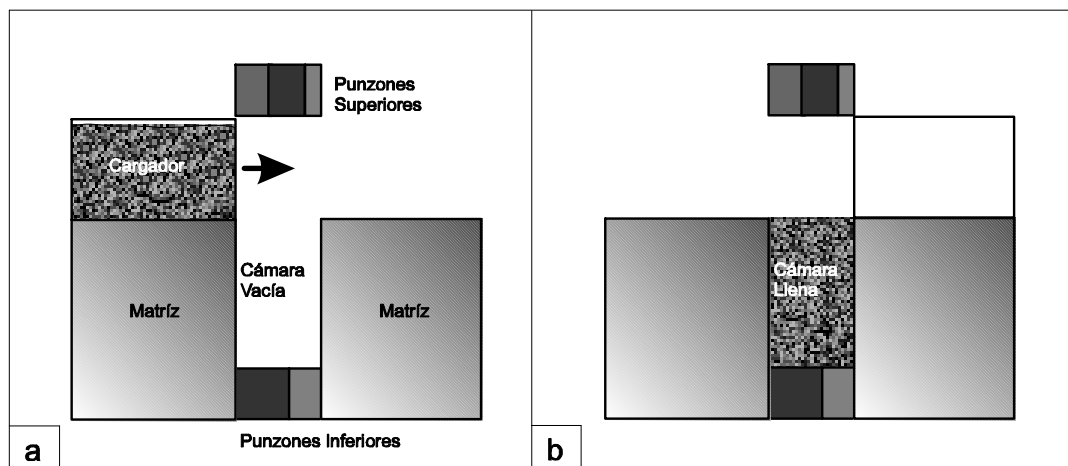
Proceso de llenado de moldes, a) material en el cargador y molde vacío, b) molde totalmente lleno de material
